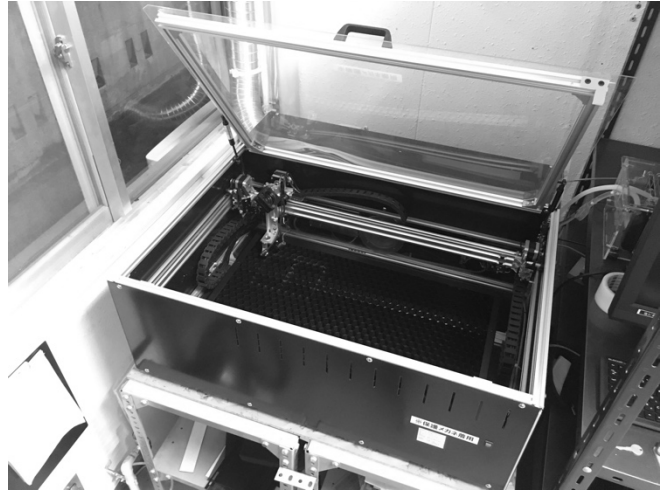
レーザー加工機の外観 (FABOOL Laser CO2)
